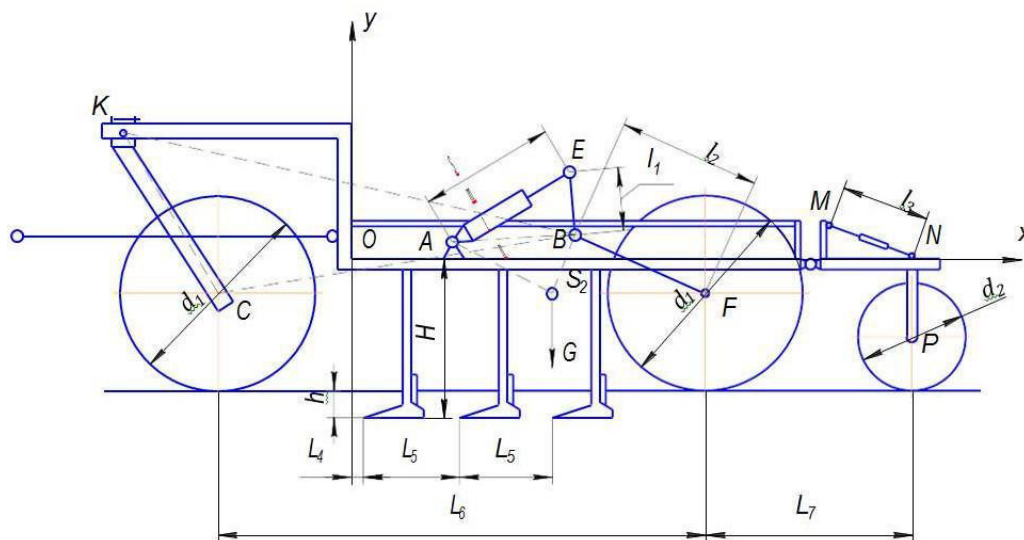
Схема механизма посевного агрегата АУП
